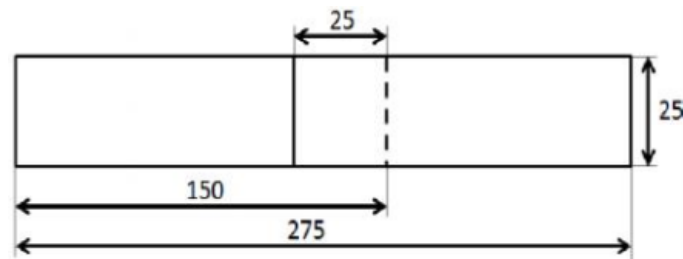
Configuration de l'assemblage en acier doux soudé par point
